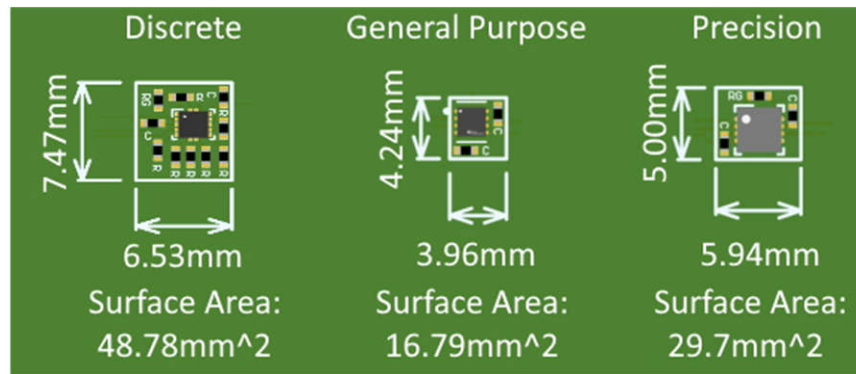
双电源 IA 电路的简化 PCB 布局比较。
